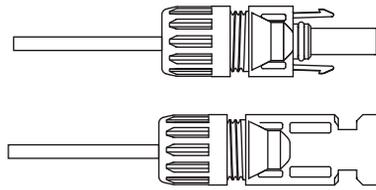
Stecker mit aufgeschraubter Überwurfmutter
